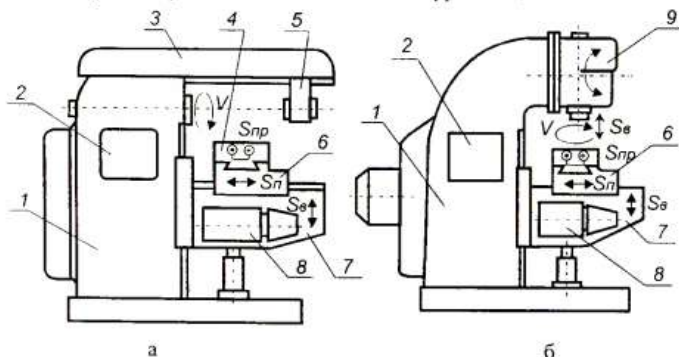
Загальний вигляд горизонтально-фрезерного (а) і вертикально-фрезерного (б) верстатів
